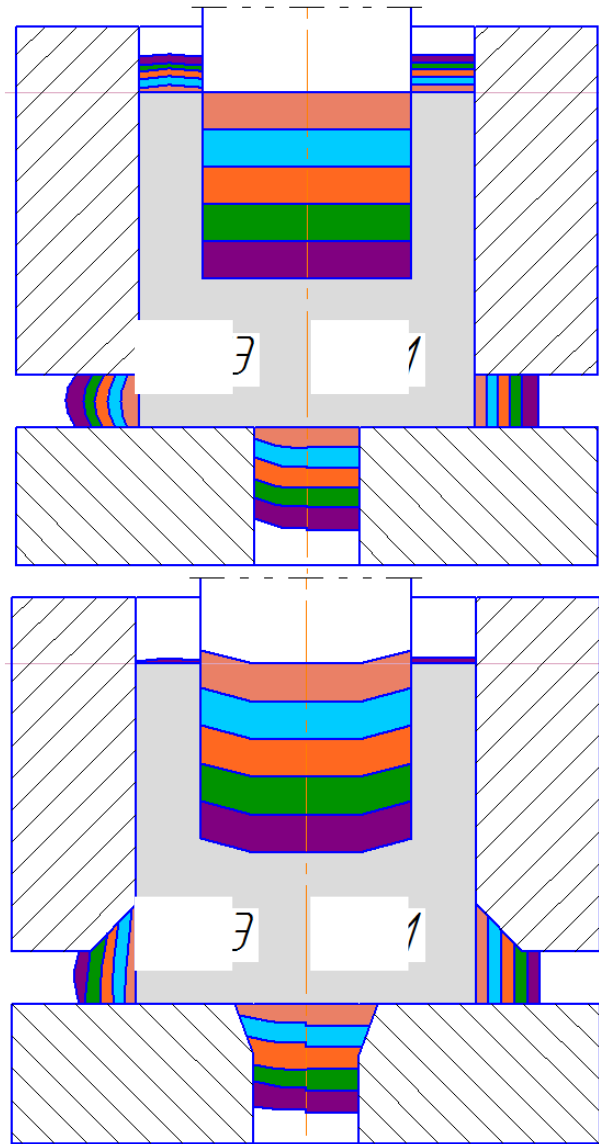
Збільшення лінійних розмірів заготовки по ходу деформування (а - схема не враховує фаски на інструменті; б – схема враховує фаски на інструменті)
